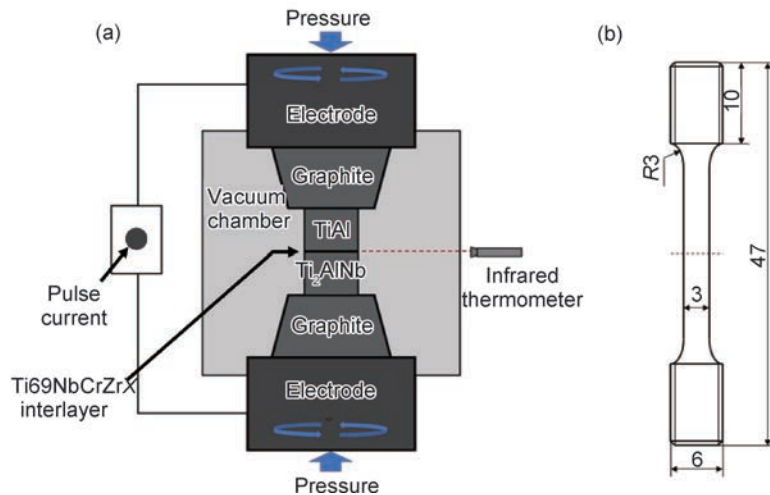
焊接设备(a)和拉伸试样(b)示意图
